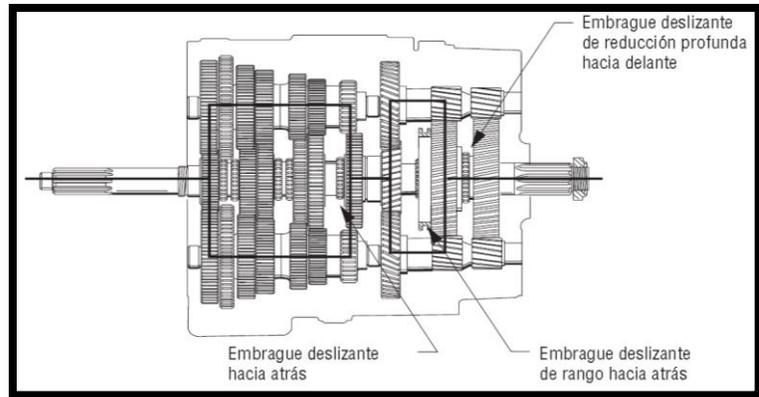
Engrane de reversa, transmisión tráiler: Fuente [34]
